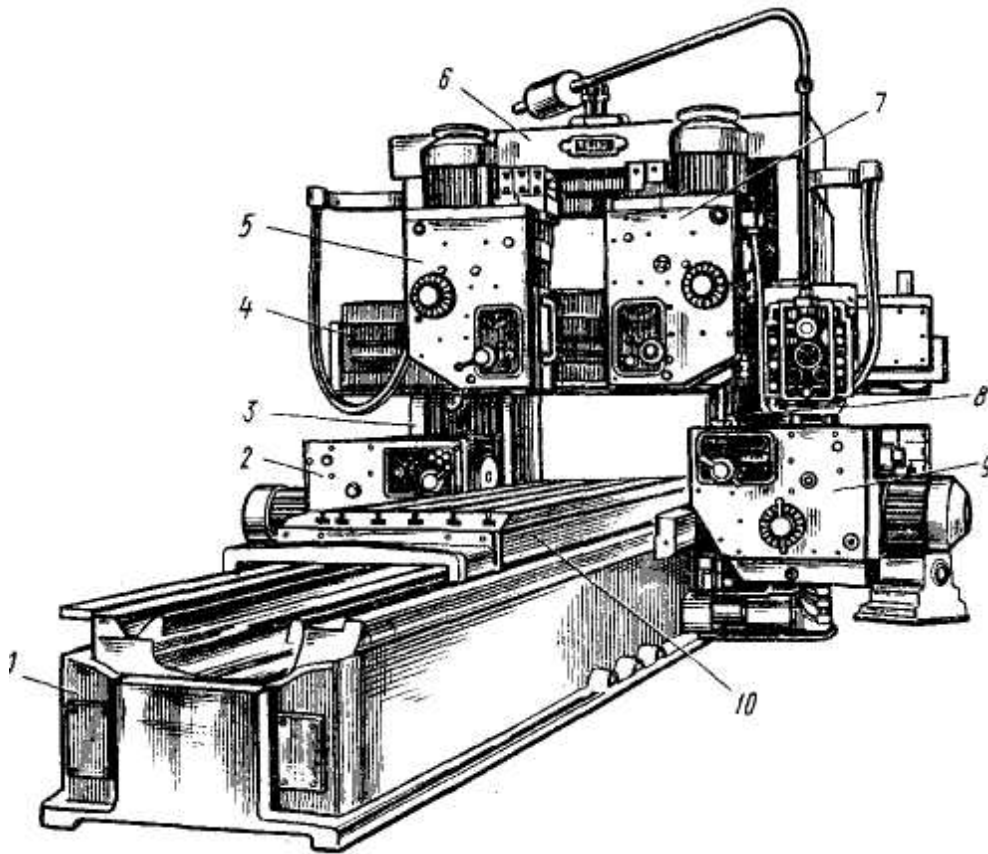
Продольно-фрезерный станок: 1 – станина; 2 – левая горизонтальная шпиндельная головка; 3 – левая стойка; 4 – траверса; 5 – левая вертикальная поворотная шпиндельная головка; 6 – балка; 7 – правая вертикальная поворотная шпиндельная головка; 8 – правая стойка; 9 – правая горизонтальная шпиндельная головка; 10 – стол
